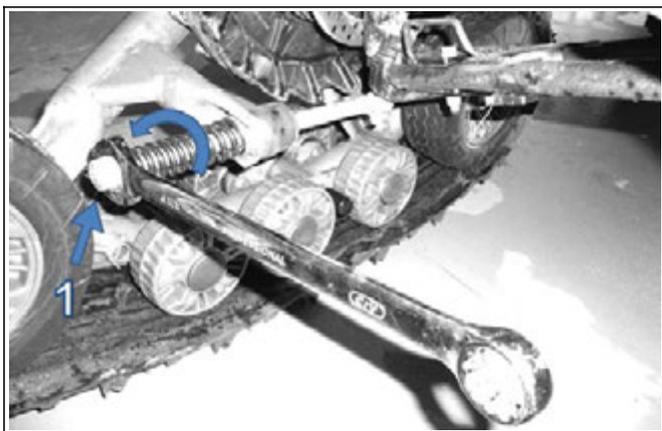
Натяжная гайка пружины выравнивающей штанги
